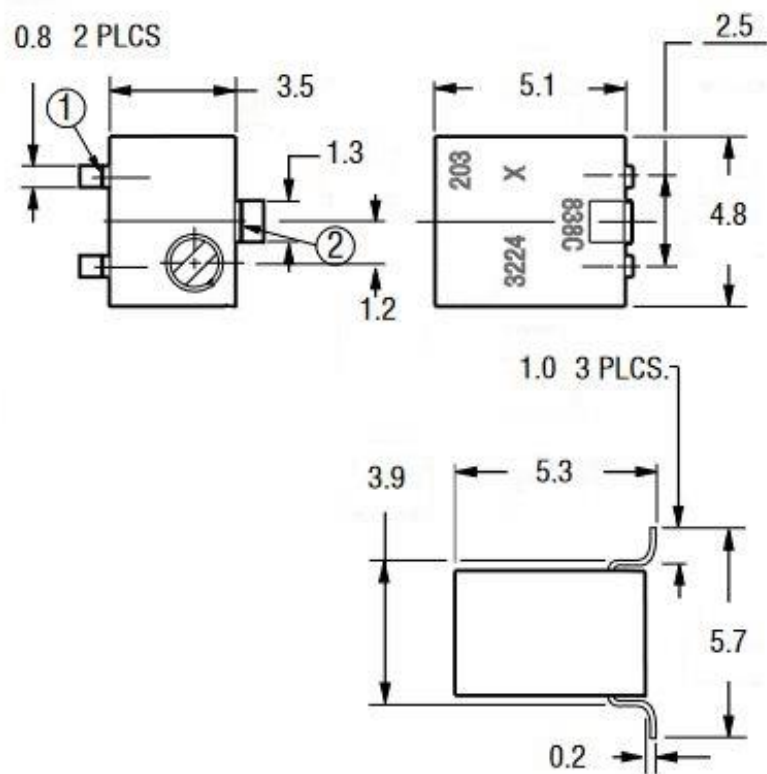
Габаритні розміри підстроювального резистора
